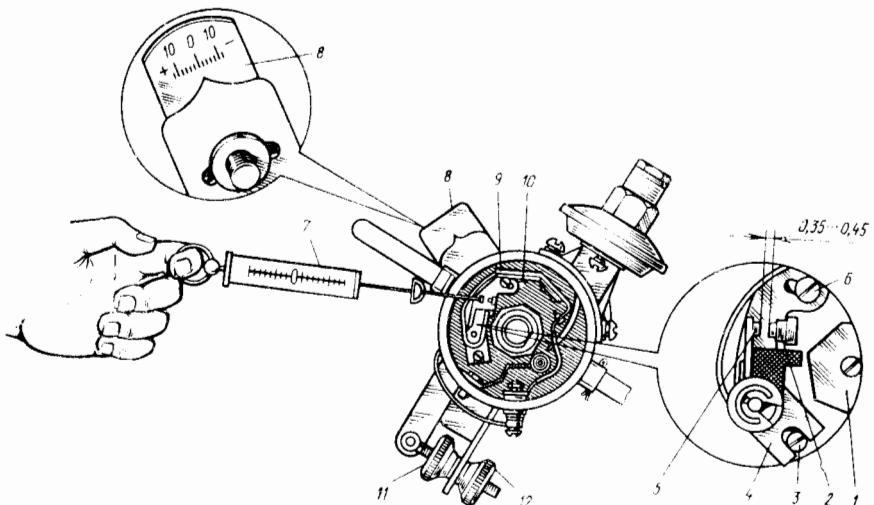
Регулировка зазора между контактами прерывателя и проверка натяжения пружины прерывателя:
